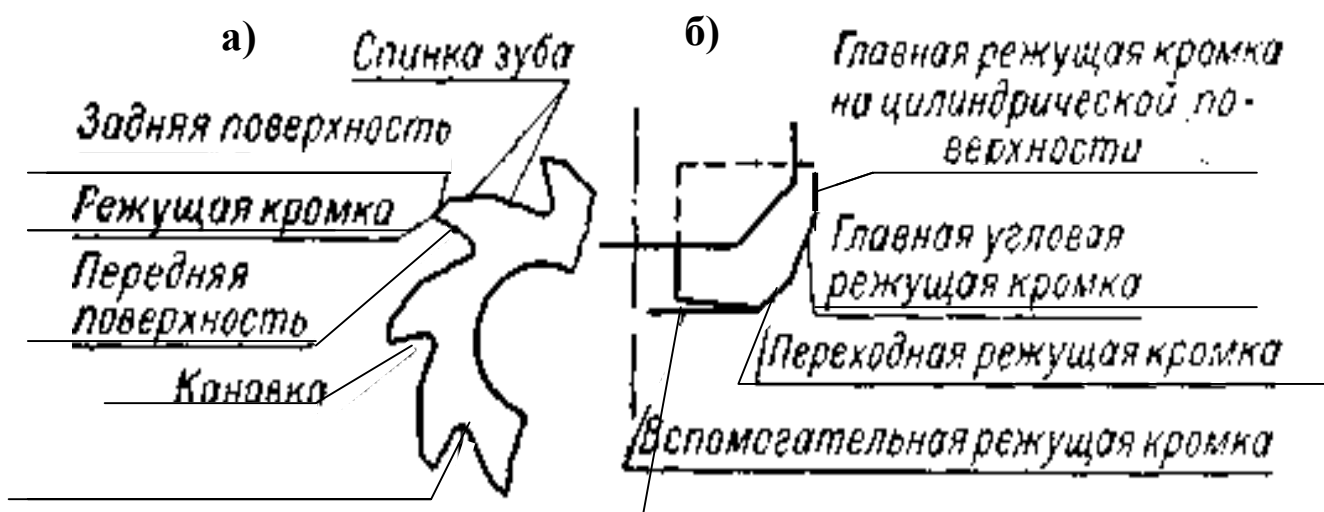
Поверхности и кромки зубьев торцевой фрезы
